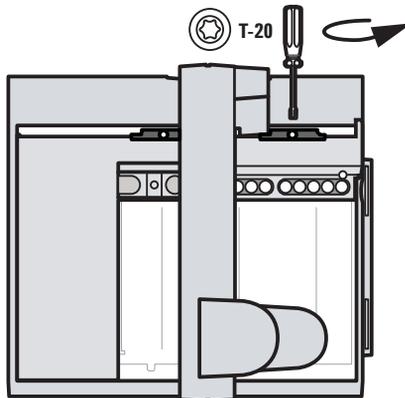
Entfernen der T-20-Schraube aus der Transportklammer
